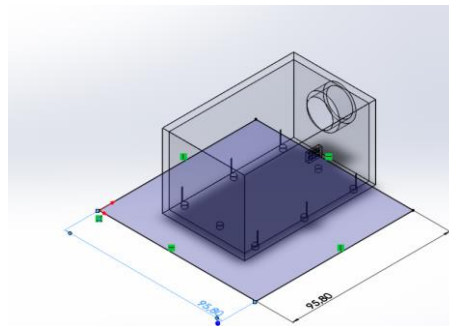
Montaje de la carcasa del sensor Argus 2000 sobre la placa de aluminio.
